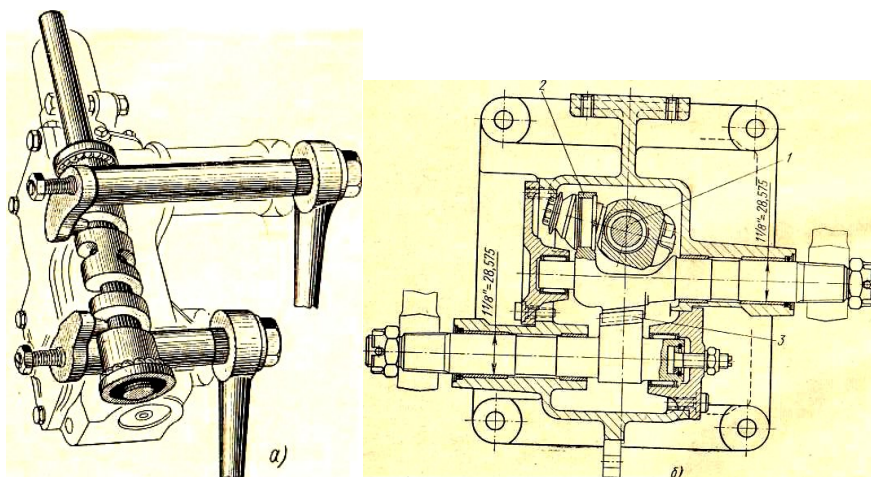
Сдвоенные рулевые механизмы с двумя кривошипами и с винтовой и зубчатой парами
